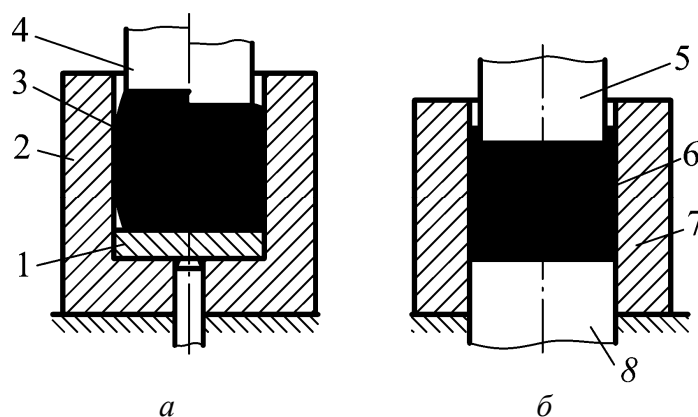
Схемы осадки в закрытом штампе: а – свободная осадка; б – осадка с образованием заусенца; 1, 8 – выталкиватели; 2, 7 – матрицы; 3, 6 – заготовки; 4, 5 – пуансоны
